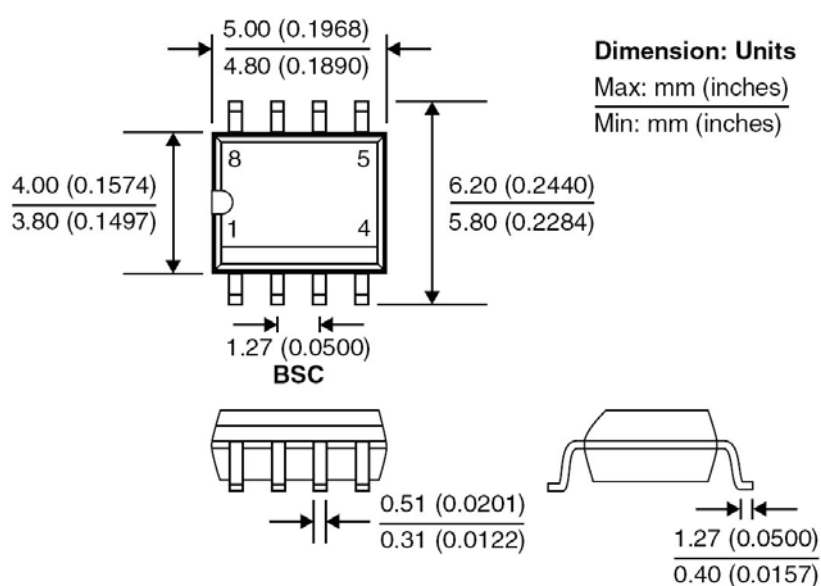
Dimensiunile componenteii așa cum le oferă producătorul
